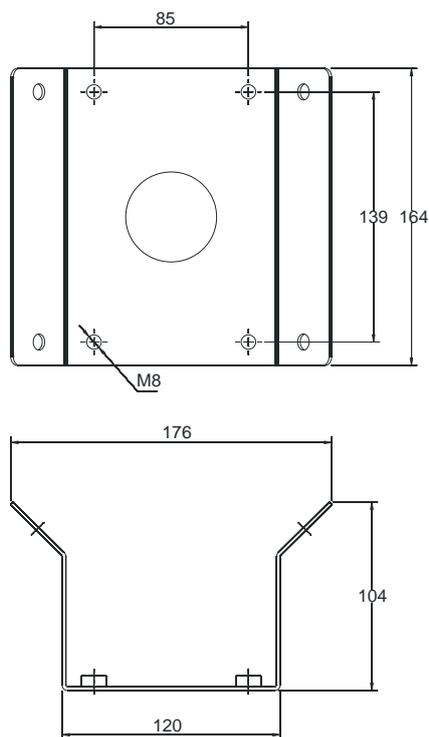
Immagine delle dimensioni del braccio di installazione ad angolo di una parete
